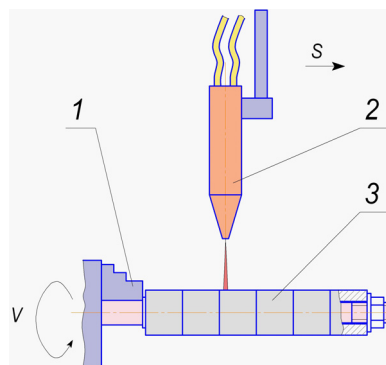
Схема процесса обработки заготовок (скорость вращателя $v = 1,5$ об/мин, скорость подачи $s = 5,45$ мм/мин)
